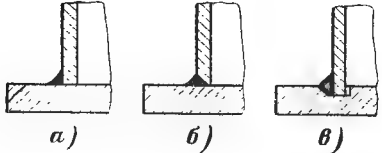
Типы сварных швов об-сачки с доньями и трубными ре-сетками.
